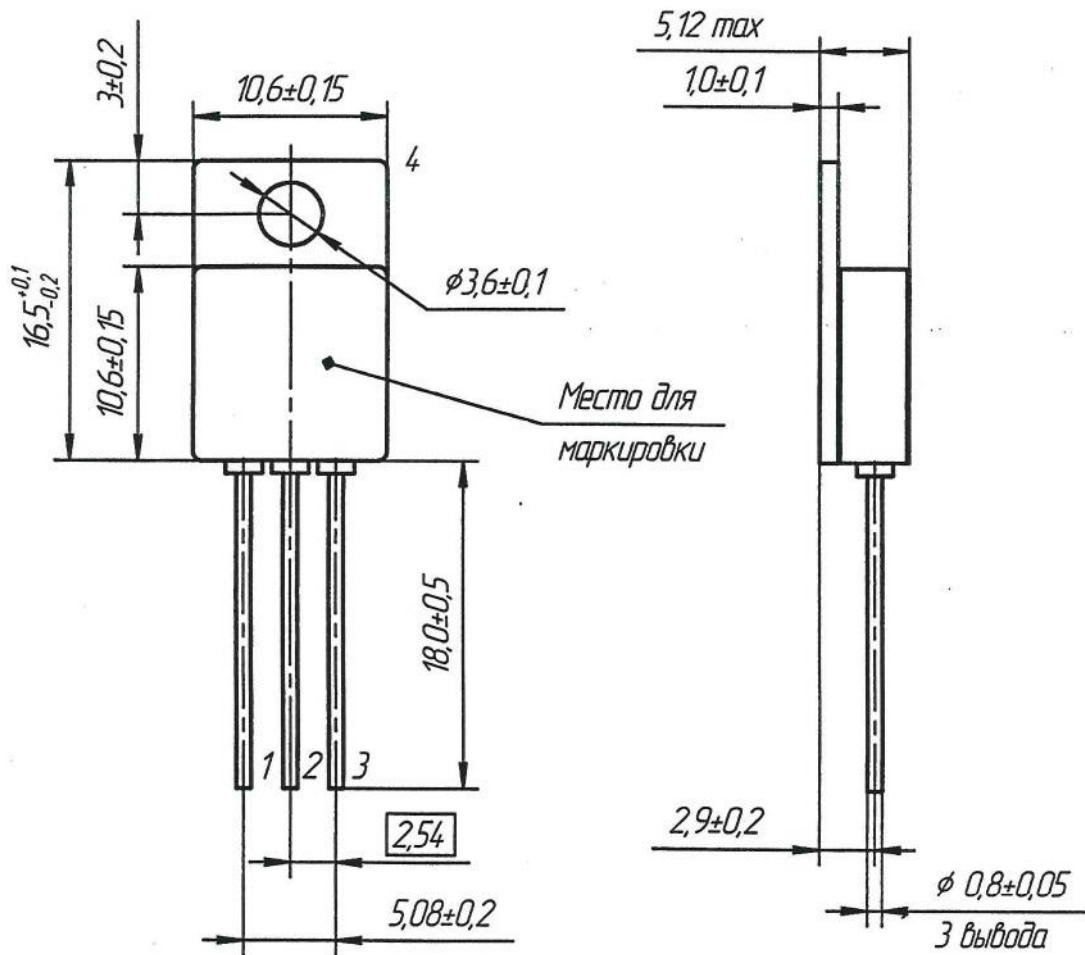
Габаритный чертеж корпуса КТ-95-1
